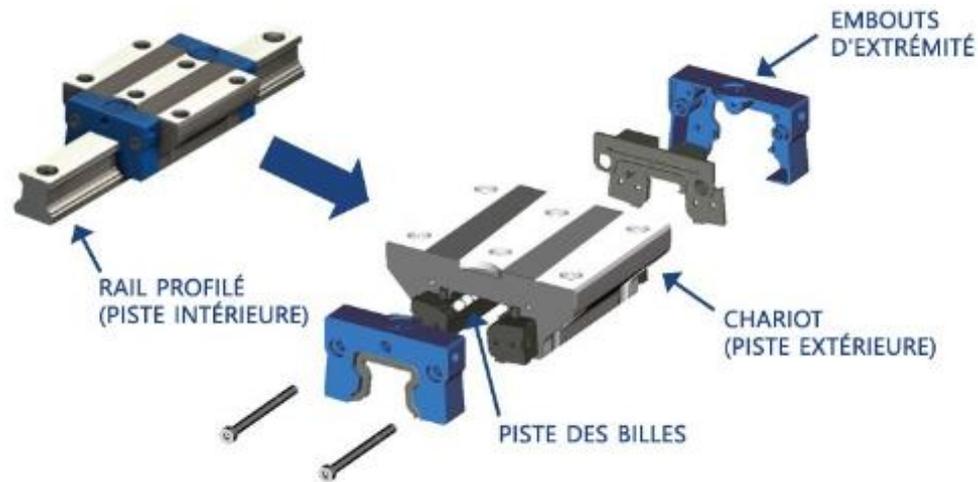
Guidage linéaire composé de rails et de patins utilisé pour l'un des axes de notre machine
